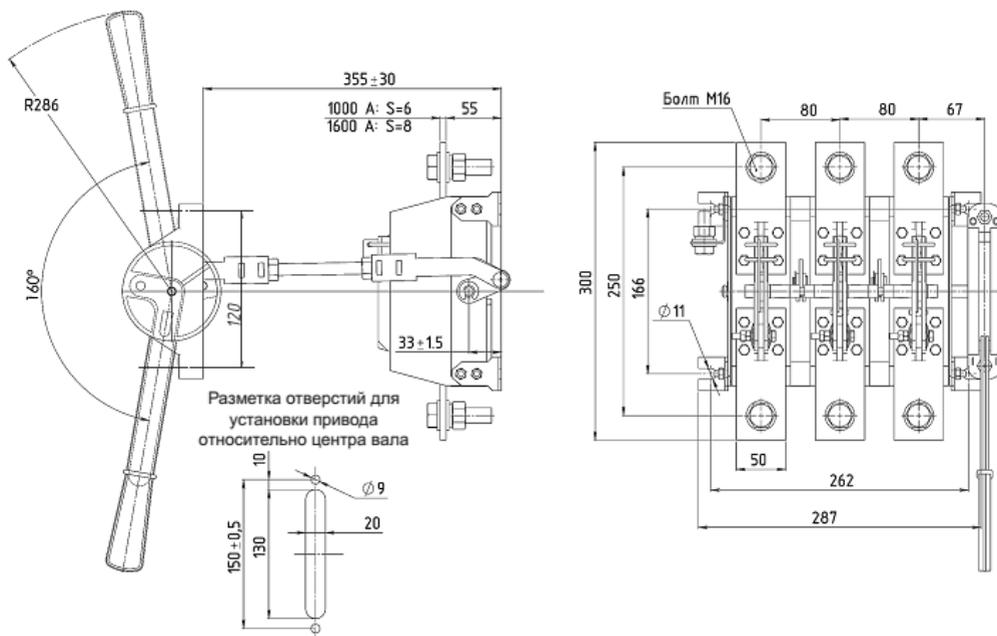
Разъединитель РЕ19-41(43)-32220-00 УХЛЗ с боковой рукояткой, заднего присоединения шин
